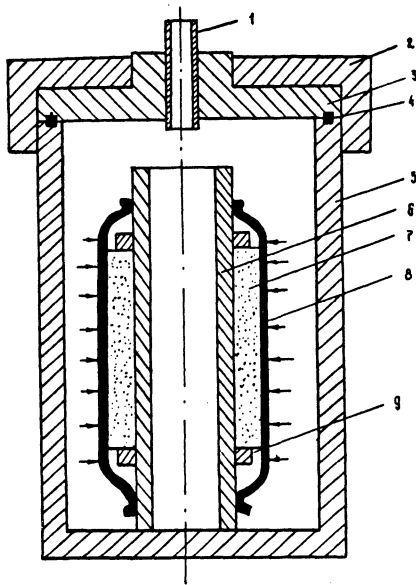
Схема гидростатического прессования полых цилиндрических заготовок:
